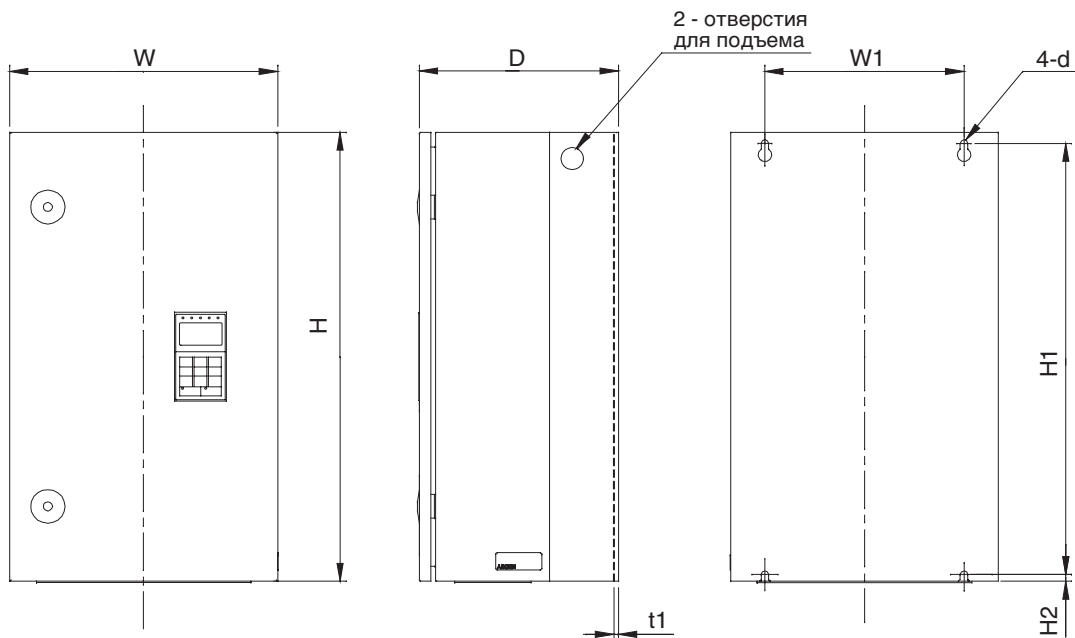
Габаритные чертежи инверторов в исполнении IP54
